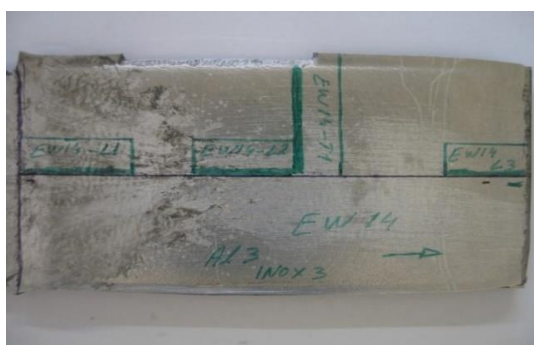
Extração de provetes na soldadura EW 14-Al.Fe-3.3.
